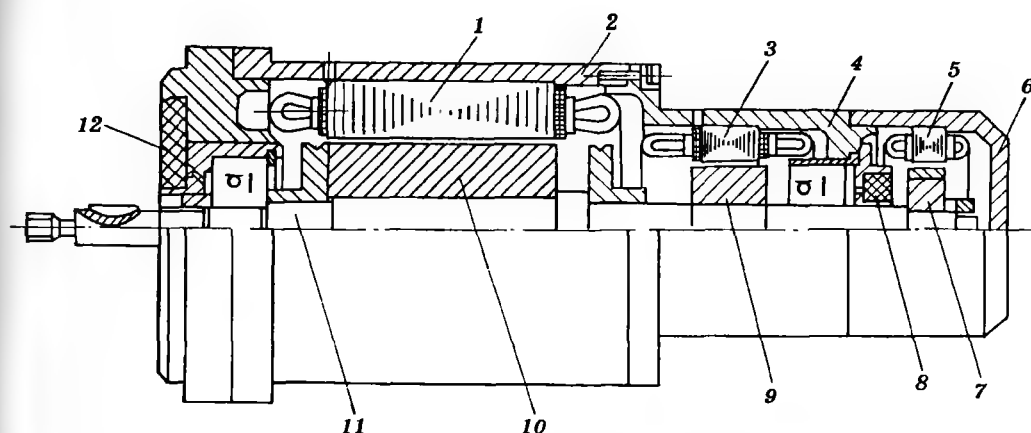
Конструкция электродвигателя ДБ60-90-6
